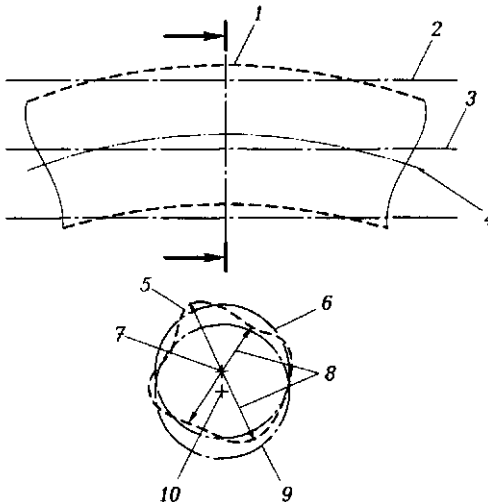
Местный размер выявленного цилиндра (местный диаметр цилиндра):
